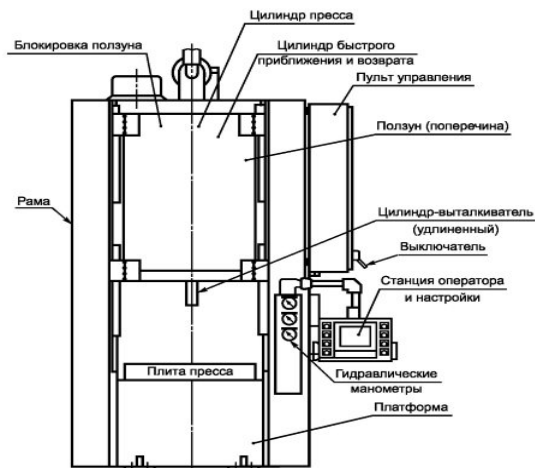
Структура экструдера для изготовления топливных брикетов из опилок с прессованием гидравлическим прессом.
